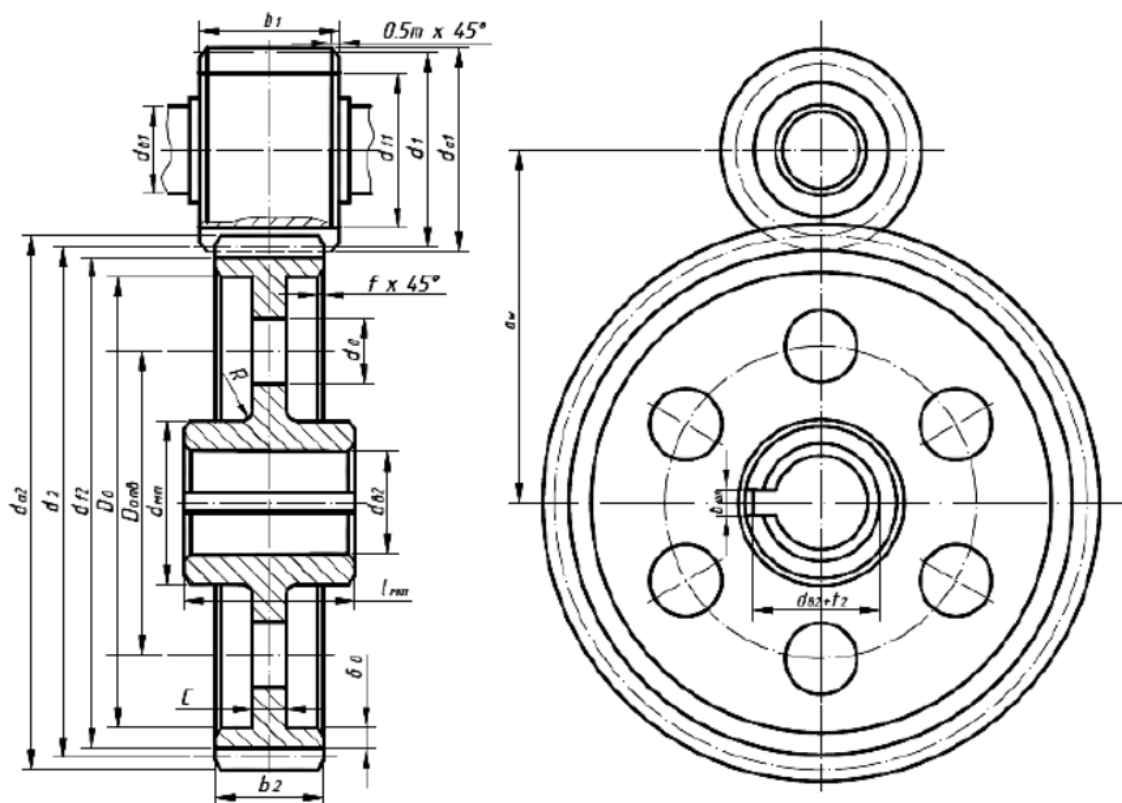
Схема зачеплення циліндричної передачі
